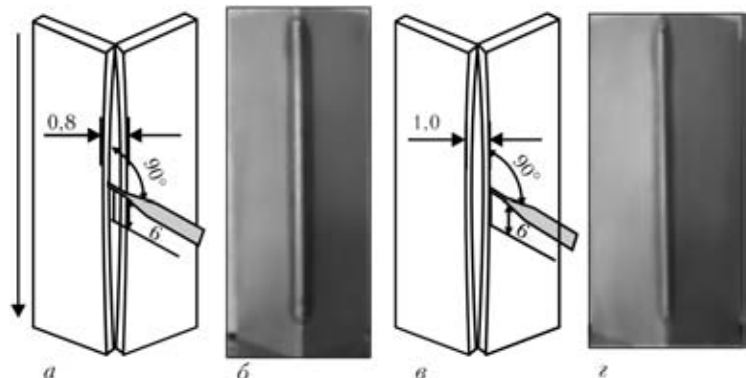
Выполнение обычной МАГ сварки при корневом зазоре в середине пластин (а, в) и внешний вид соединений (б, г)
